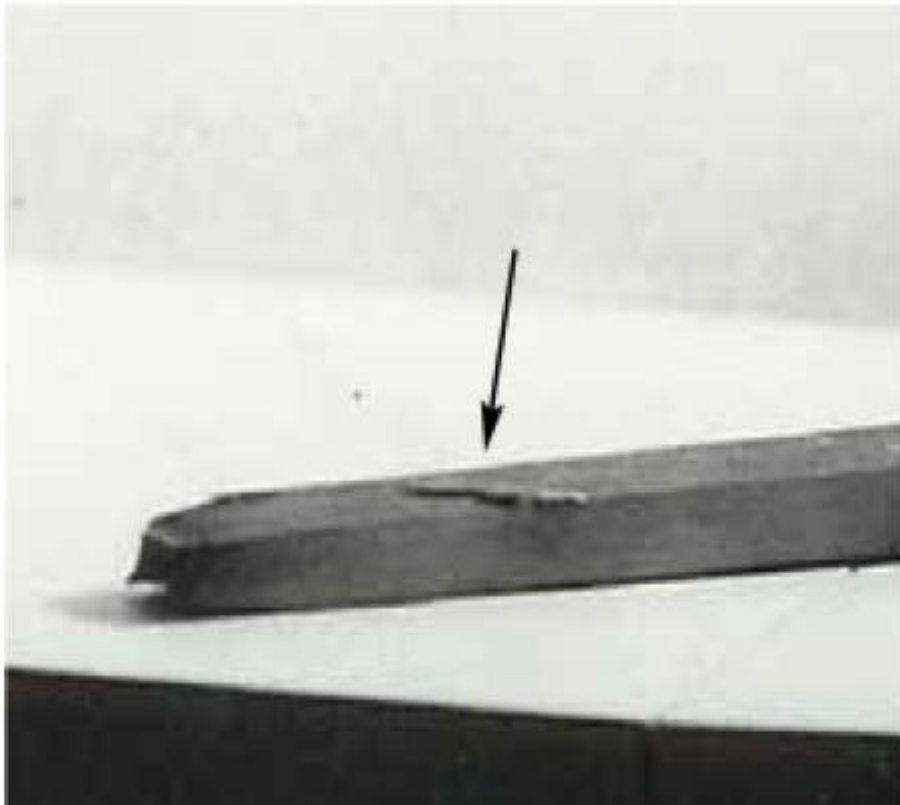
Pailles sur éprouvette d'essai et sur ouvrage
